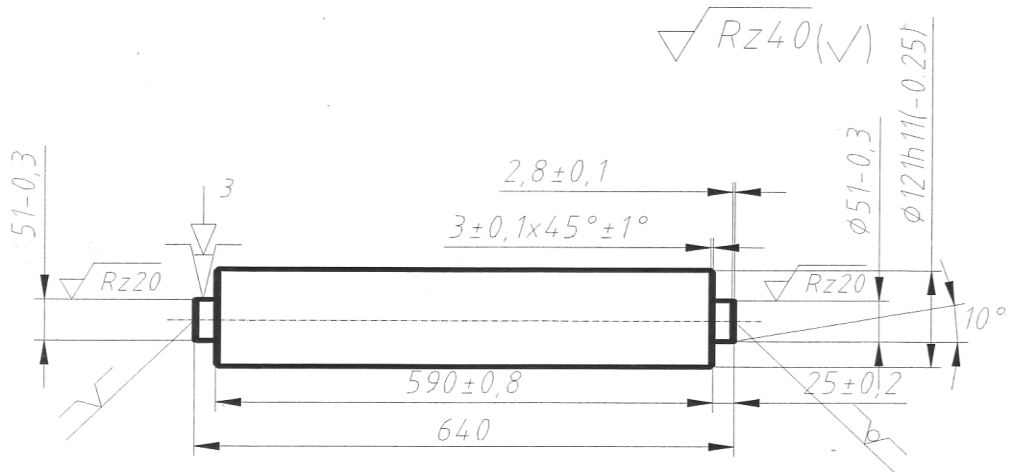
Ескіз обробки деталі операція №030
